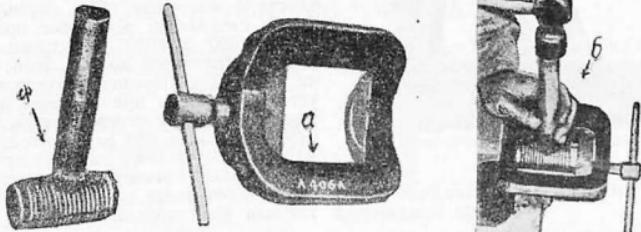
Ф — уплотнитель баббита; а — пресс, зажимающий бортики 3-го подшипника; б — уплотнение баббита в 3-м подшипнике
